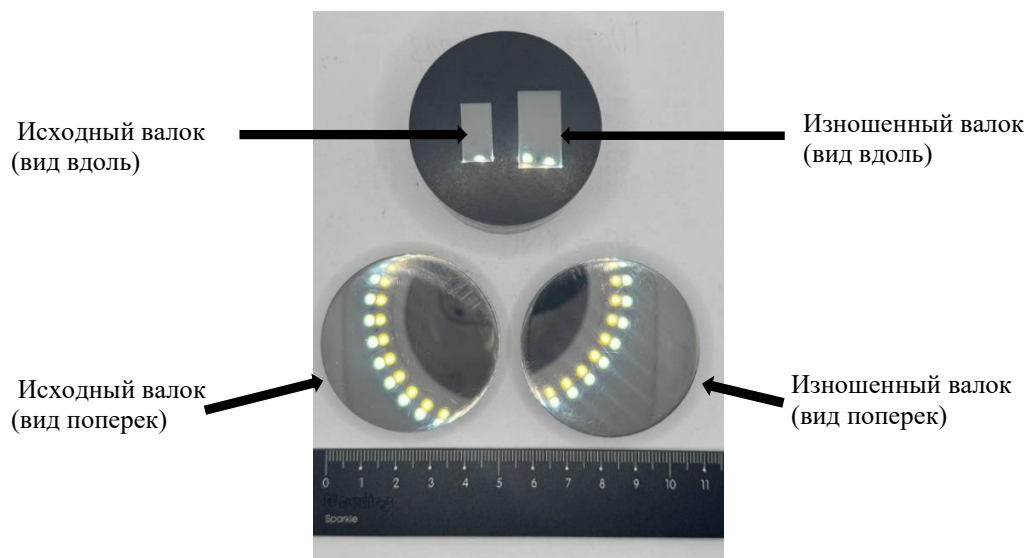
Образцы после шлифовки и полировки (фото автора)
